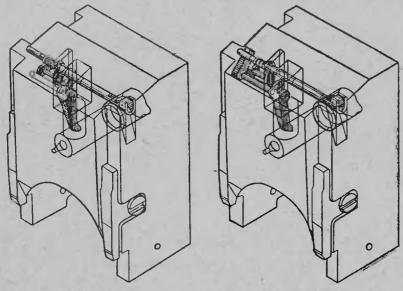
Положение деталей ударного и предохранительного механизмов при сборке (третья операция)
